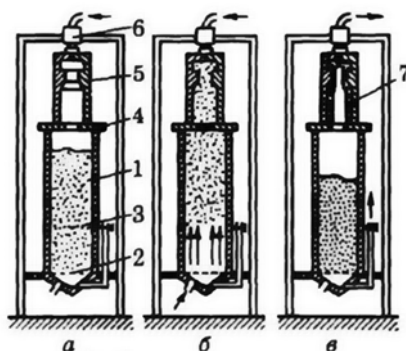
Схема пескодувного способа изготовления оболочкового стержня
